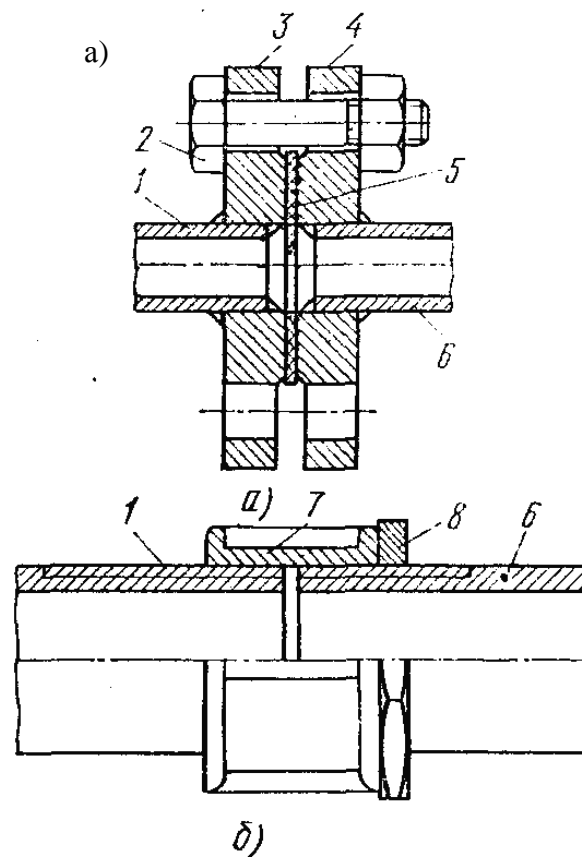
Фланцевое (а) и муфтовое (б) соединения трубопроводов:
